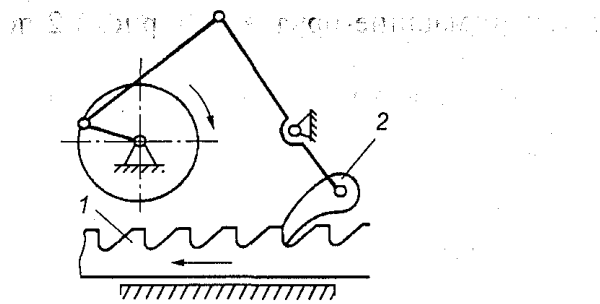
Нереверсивний храповий механізм: 1 - рейка; 2 - собачка
